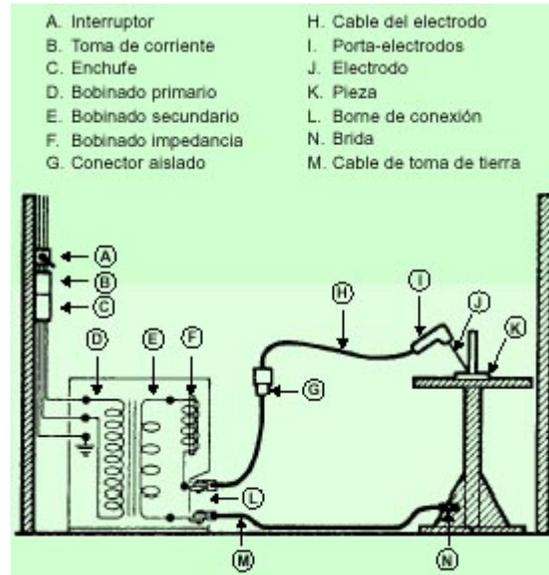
Instalación segura de un puesto de soldadura CA con transformador
